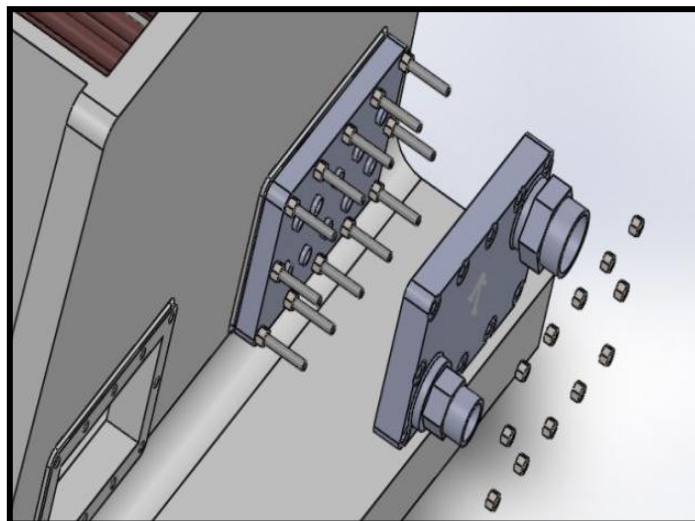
mur dan besi ulir *cover oil cooler turbne guide bearing
